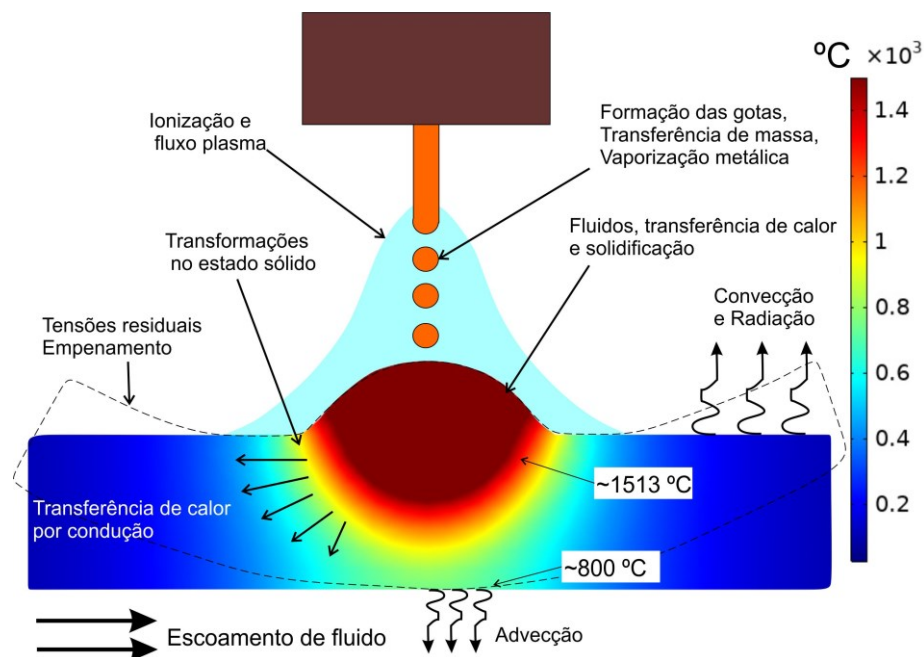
Esquemático da multifísica da soldagem. Fonte: O próprio autor.
